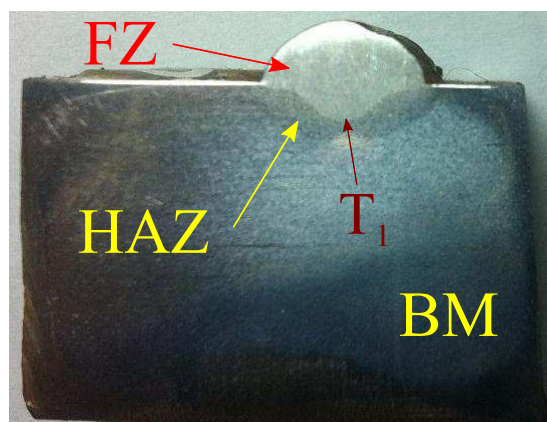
Corte transversal de un cordón de soldadura. Se muestran las zonas de soldadura y la ubicación de la termocupla T_1 .
